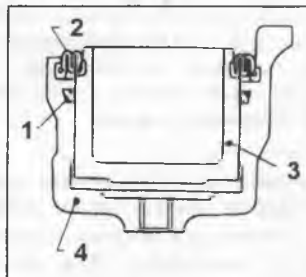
1. Уплотнительное кольцо. 2. Защитный колпачок. 3. Поршень. 4. Цилиндр.
